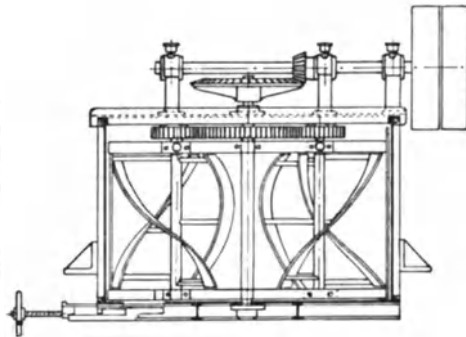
Planetenrührwerk mit Bandrührwerkzeugen.
